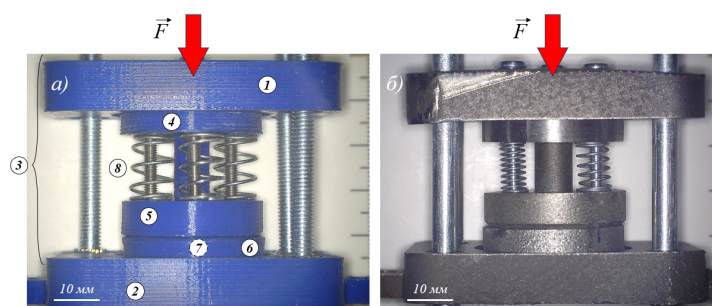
Деформирующий инструмент для микровытяжки в сборе: полимерный (а) и металлический (б) варианты исполнения.
